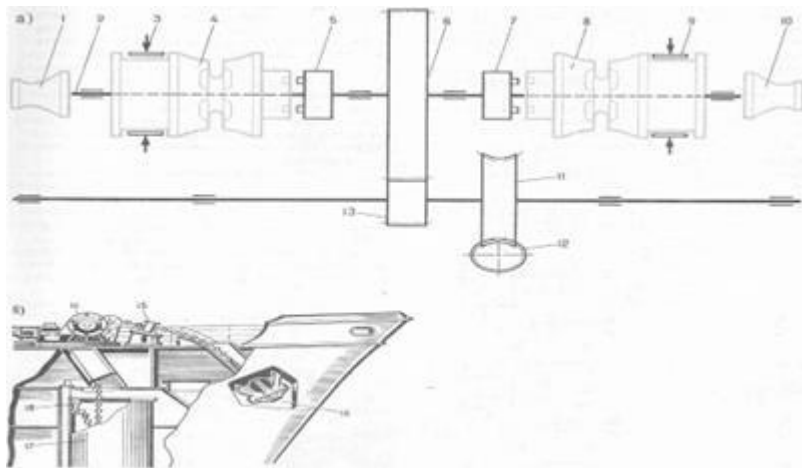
Устройство электрического брашпиля: 1,10 - швартовные турачки; 2 - грузовой вал; 3,9 - ленточные тормоза; 4,8 - цепные звездочки; 5,7 - кулачковые муфты; 6,13 - цилиндрические шестерни; 11,12 - червячная передача; 14 - брашпиль; 15 - цепной стопор; 16 - клюз; 17 - цепной ящик; 18 - жвакагалс.
